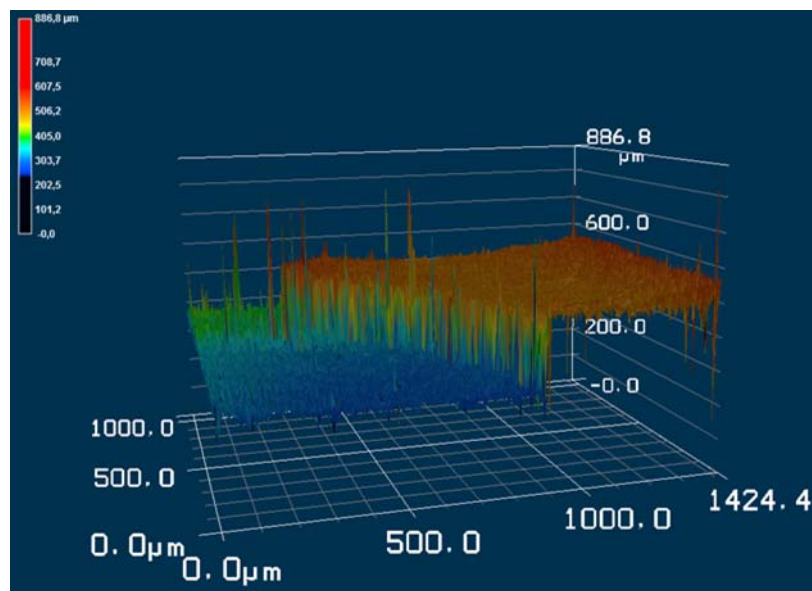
3-dimensionale Darstellung einer LSM-Messung. Erkennbar ist der Absatz auf einer Bohrfläche, der durch die Verschweißung von Material auf der Oberfläche zustande kommt.
